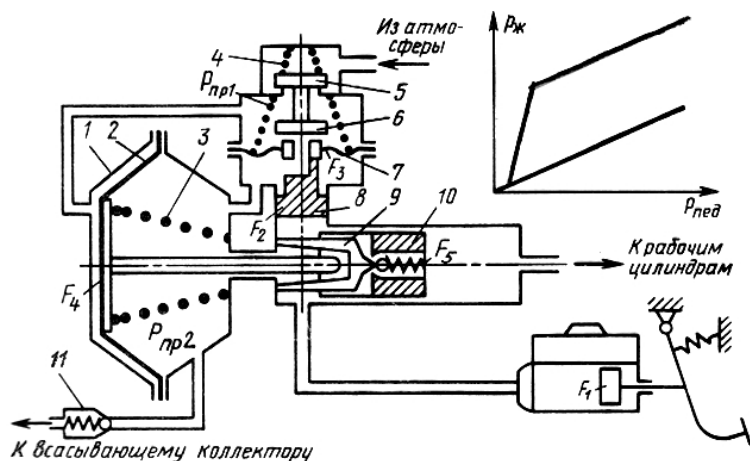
Схема гидровакуумного усилителя с мембранным следящим механизмом и его статическая характеристика: 1 — камера; 2 — диафрагма; 3 и 4 — пружины; 5 — атмосферный клапан; 6 — вакуумный клапан; 7 — мембрана; 8 — поршень следящего механизма; 9 — толкатель; 10 — поршень гидроцилиндра
